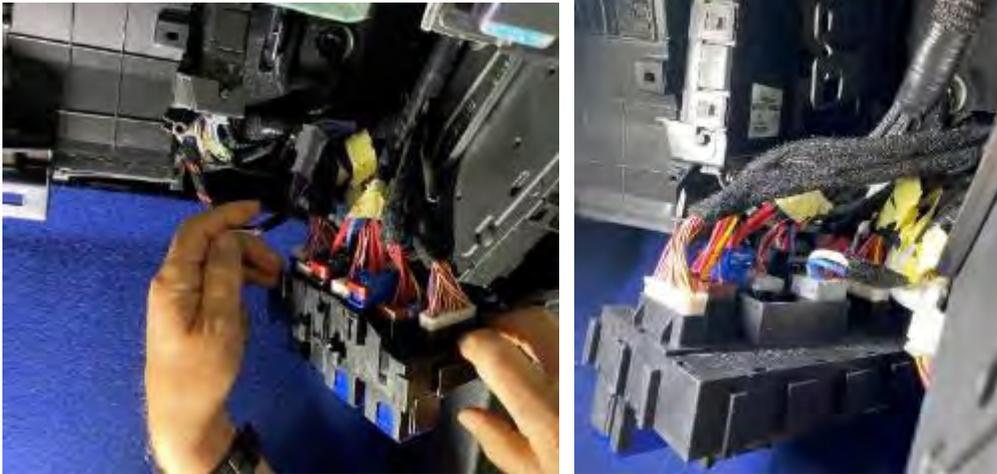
Conjunto del soporte de fusibles.
